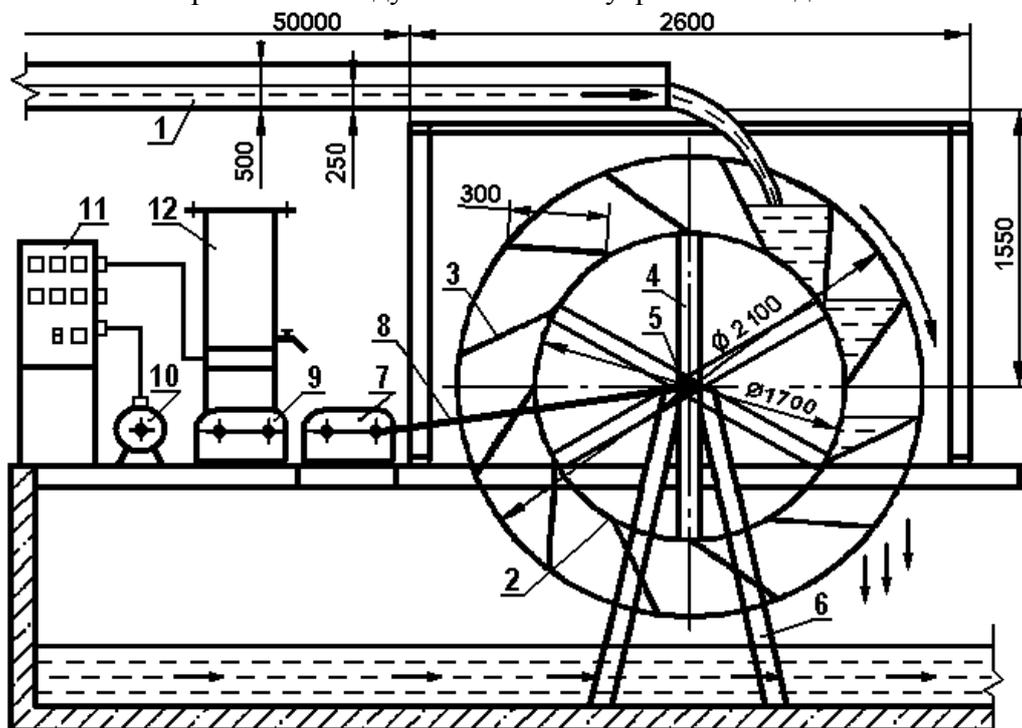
Фото водоналивного колеса и подводящего лотка (вид сбоку)
